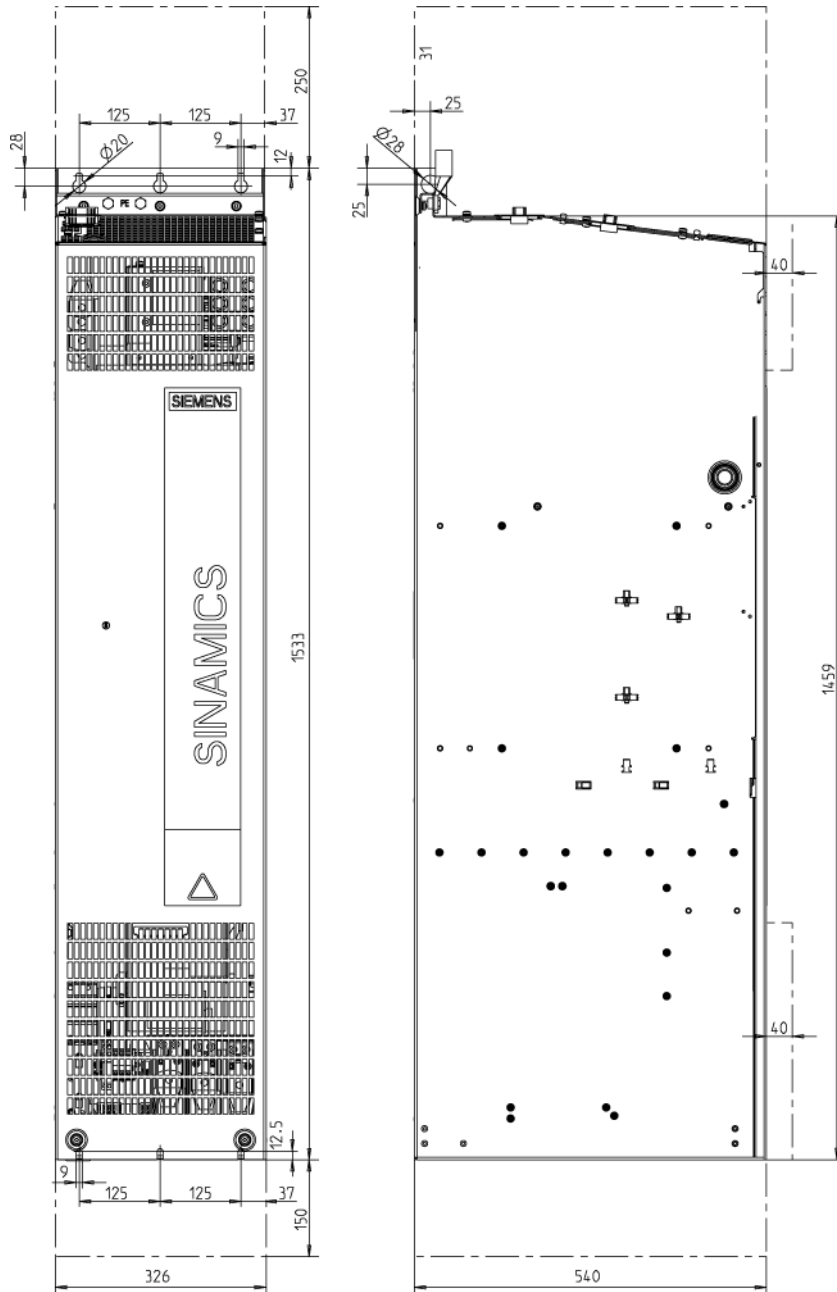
GX 型电机模块的外形尺寸图 正视图和侧视图
